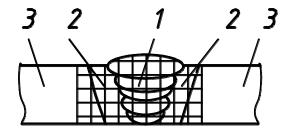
Макрошлифы сварных соединений с координатной сеткой (размер ячеек 2×2 мм): 1 -шов; 2 - 3ТВ; 3 - основной металл
